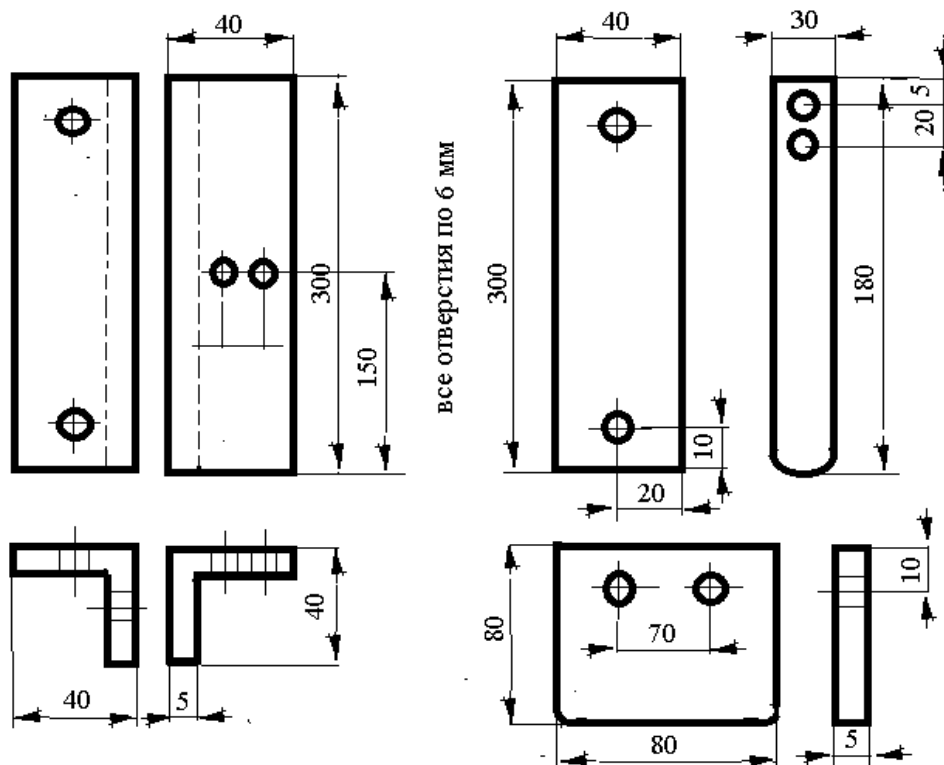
Чертеж приспособления для гибки тонколистового металла
